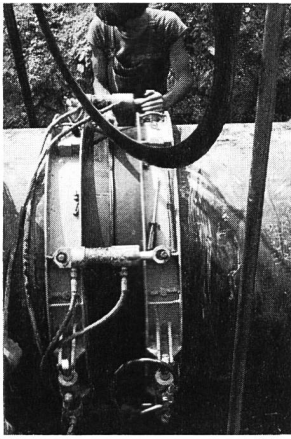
Schweissmaschine für Rohre mit 1200 mm Durchmesser.
